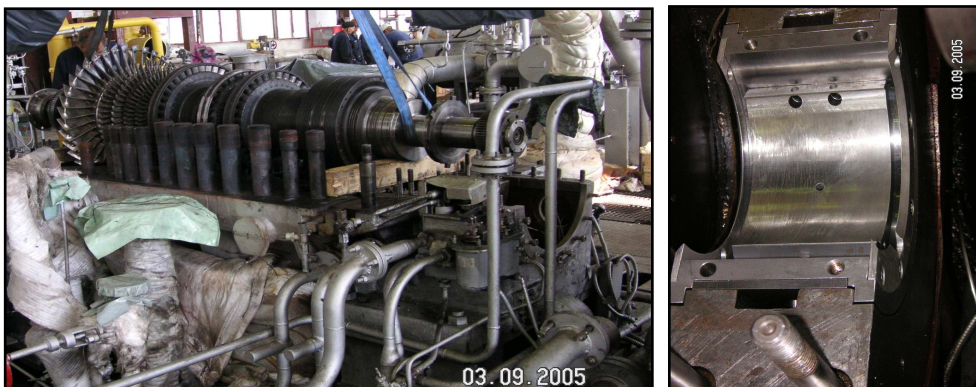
Установка ротора турбины на демпферные опорные подшипники ПД122- ТРИЗ®.
